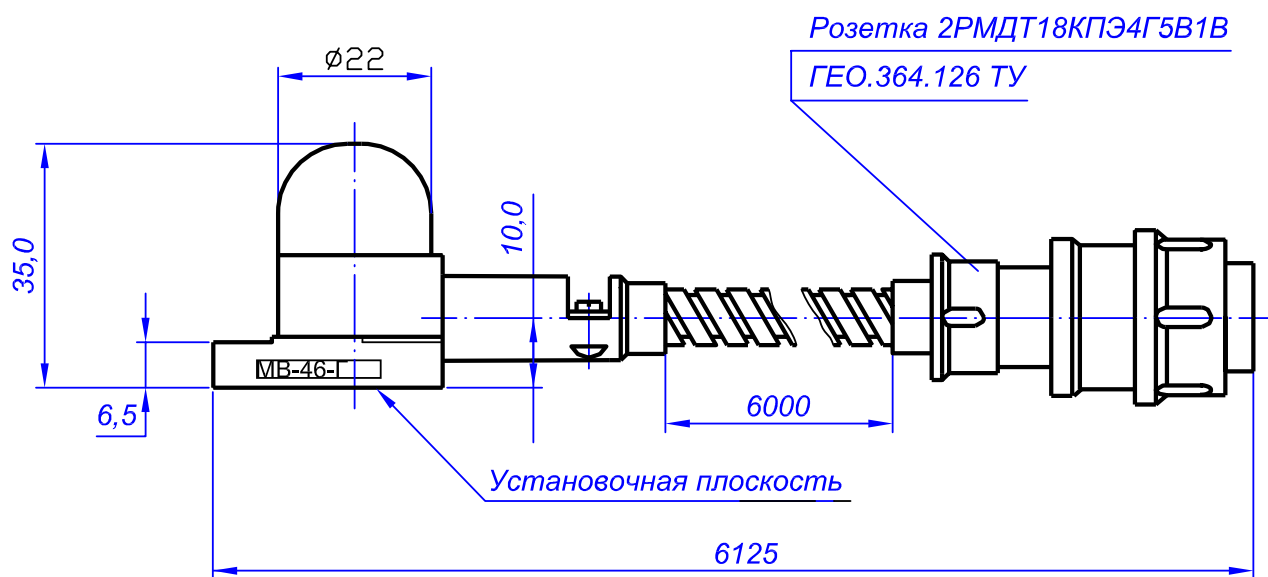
Габаритно-установочные размеры вибропреобразователя MB-46-Г/6,0
